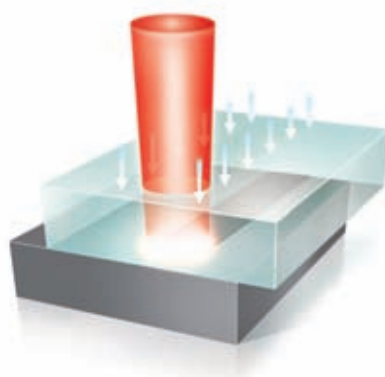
Схема лазерной сварки ПМ просвечиванием: верхняя деталь прозрачна для лазерного излучения, а нижняя непрозрачна и нагревается, поглощая энергию лазерного излучения (фото: LPKF)
